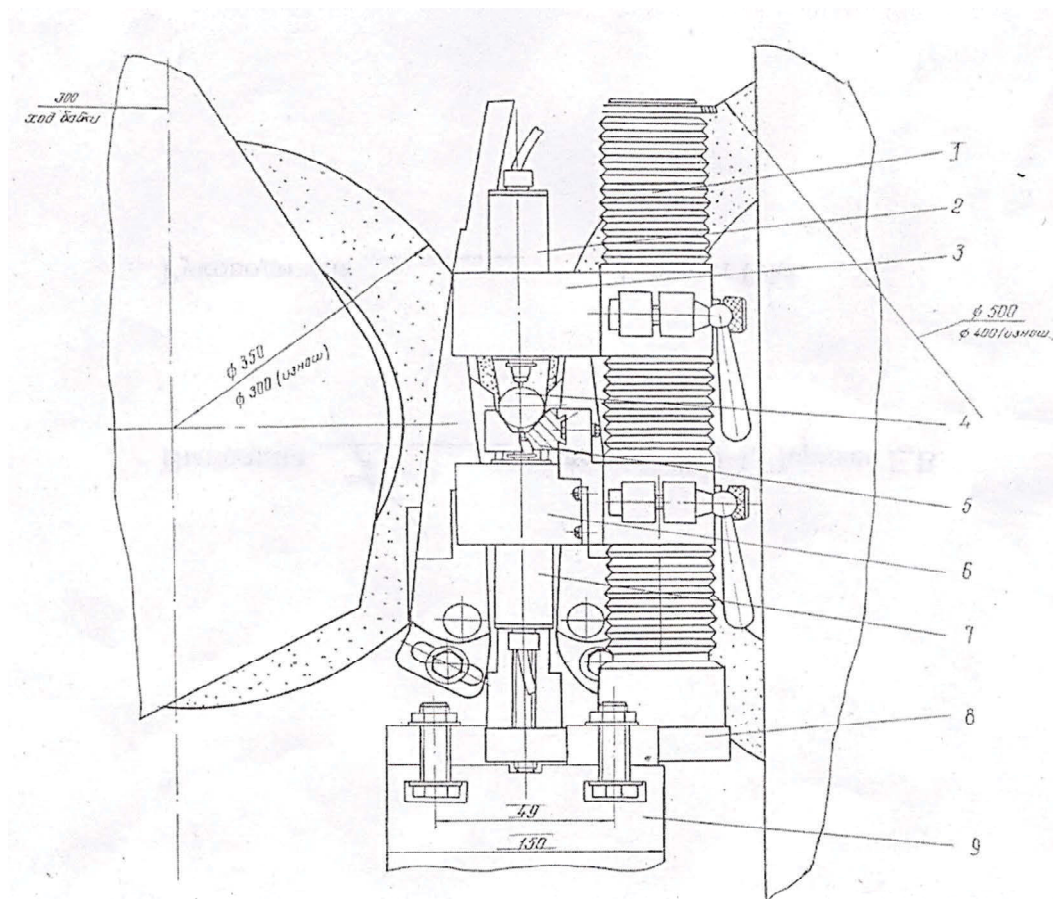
Измерительная оснастка прибора автоматического активного контроля ЛАК-9-УПИ (патент № 66514) на стане бесцентрово-шлифовального станка
